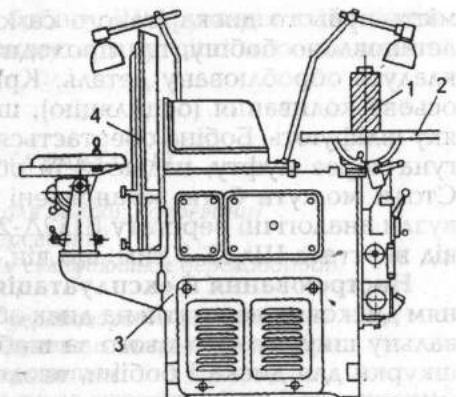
Дисковий шліфувальний верстат ШЛДБ-3:
